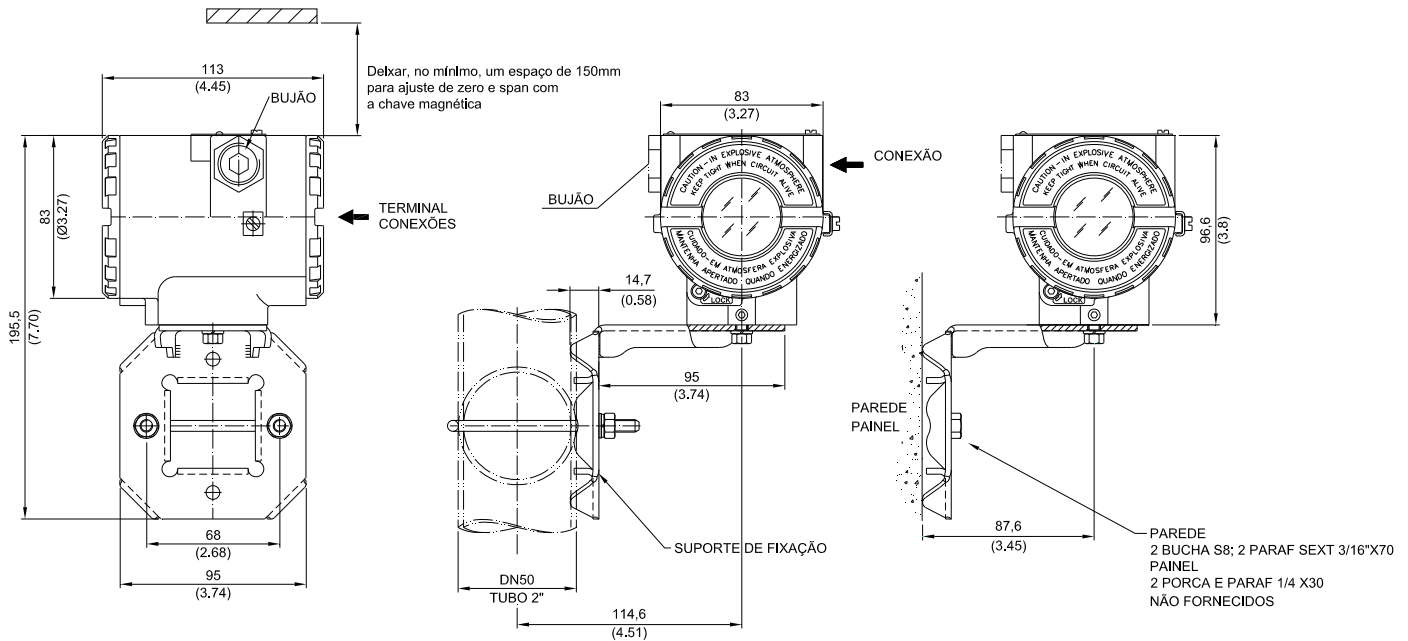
Posições de Montagem e Desenho Dimensional
